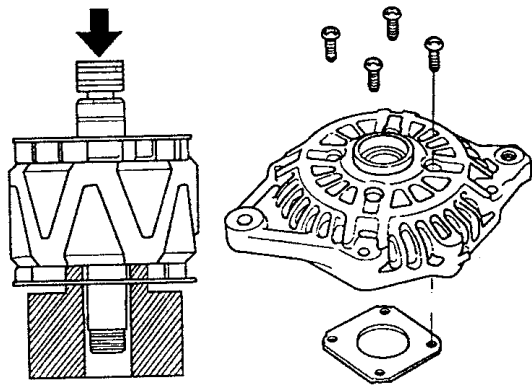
安装后轴承 图 9-52 拆卸前轴承护圈板
